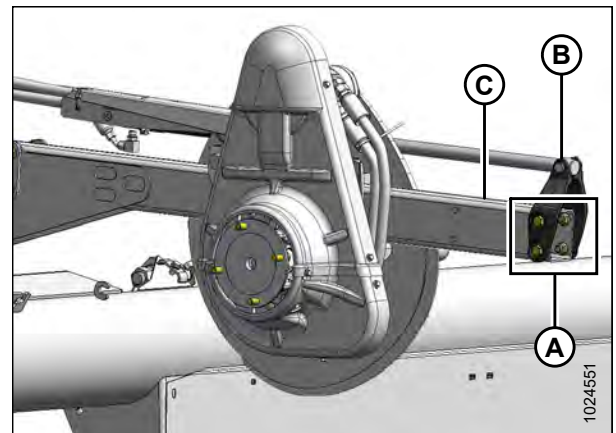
Mittlerer Haspelarm – Stellung „Vorne“
